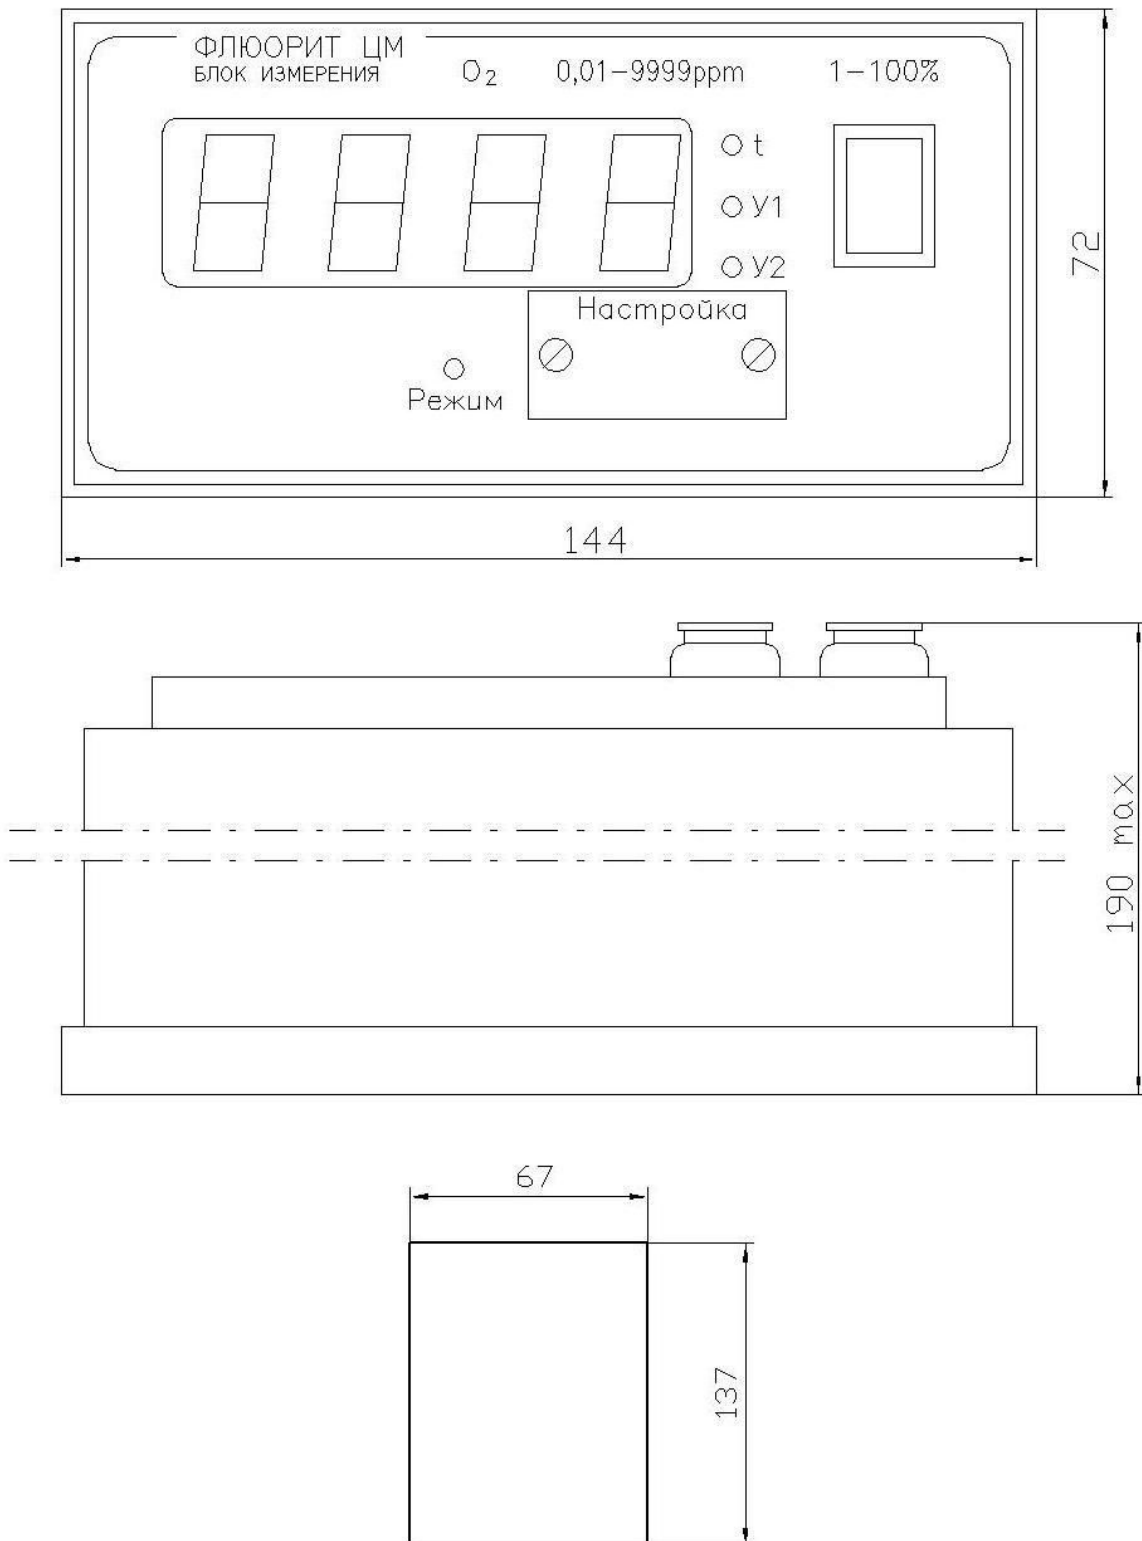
Габаритно-установочный чертеж блока измерений ИСП1
